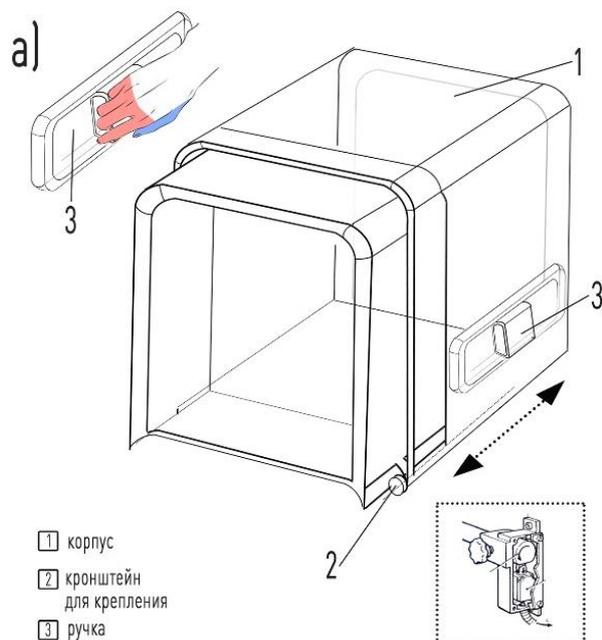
Защитный кожух: 1 – металлический корпус; 2 – рельсовые направляющие; 3 – ручка
